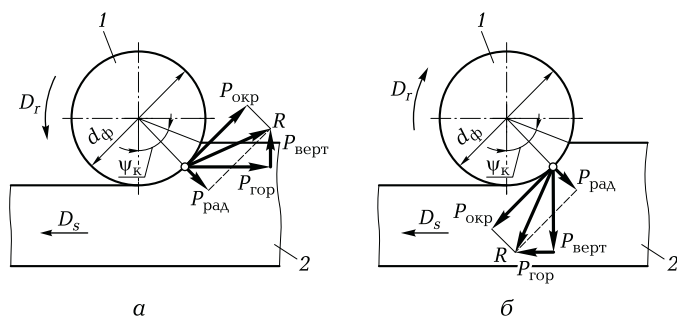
Силы, действующие на заготовку при встречном (а) и попутном (б) фрезеровании:
